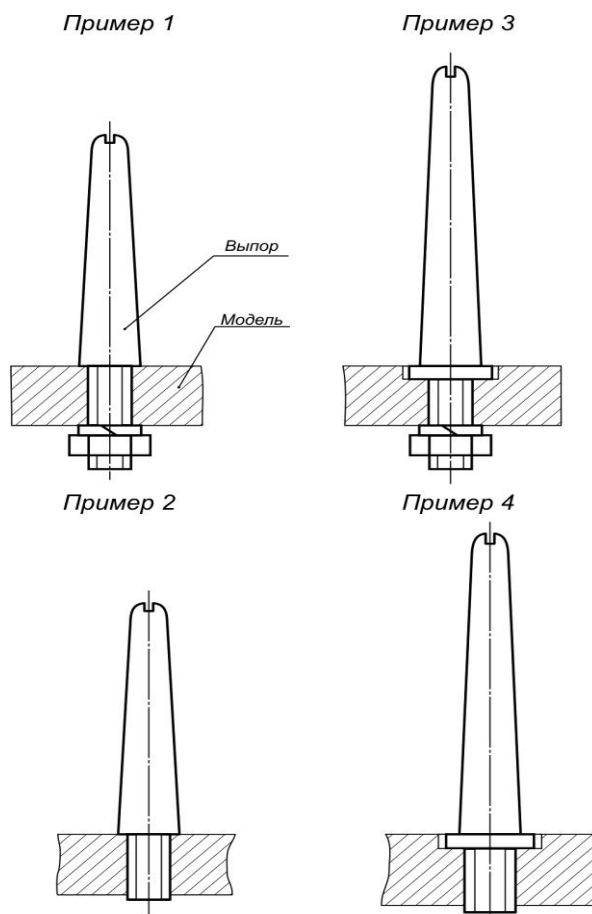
Примеры установки газоотводных выпоров на моделях отливки
